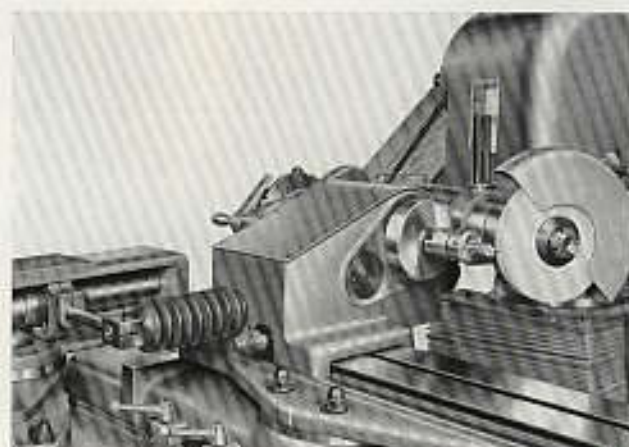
, Hinterschliffen des Anschnittes an einem Gewindebohrer
